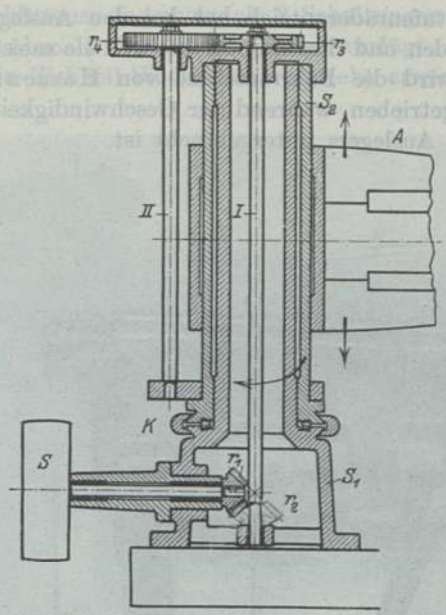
Säule der Hessemüllerschen Auslegerbohrmaschine.
